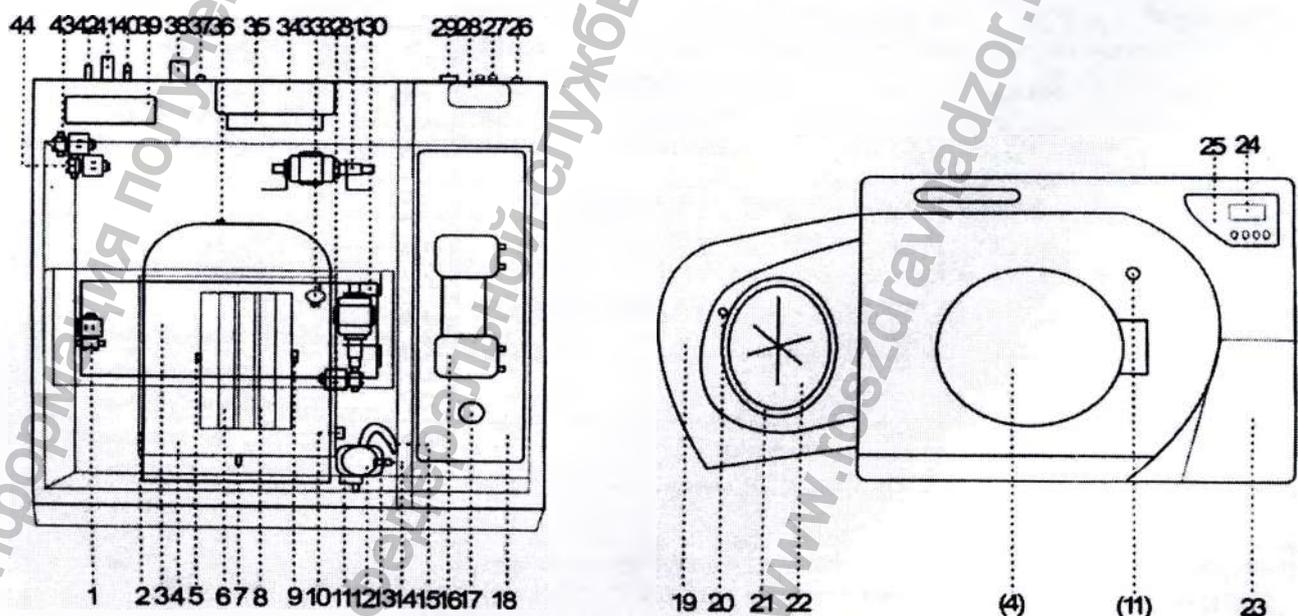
Чертеж Стерилизатора парового T&S17B
